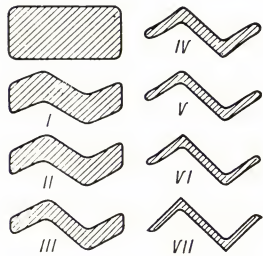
Схема изменения сечения (калибровка) при прокатке зетообразного профиля.
